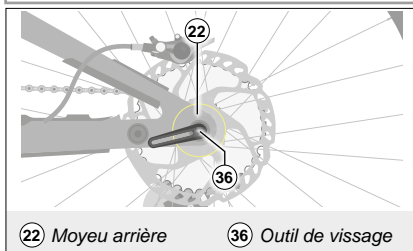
Outil de vissage de la batterie sur l'axe de la roue arrière
